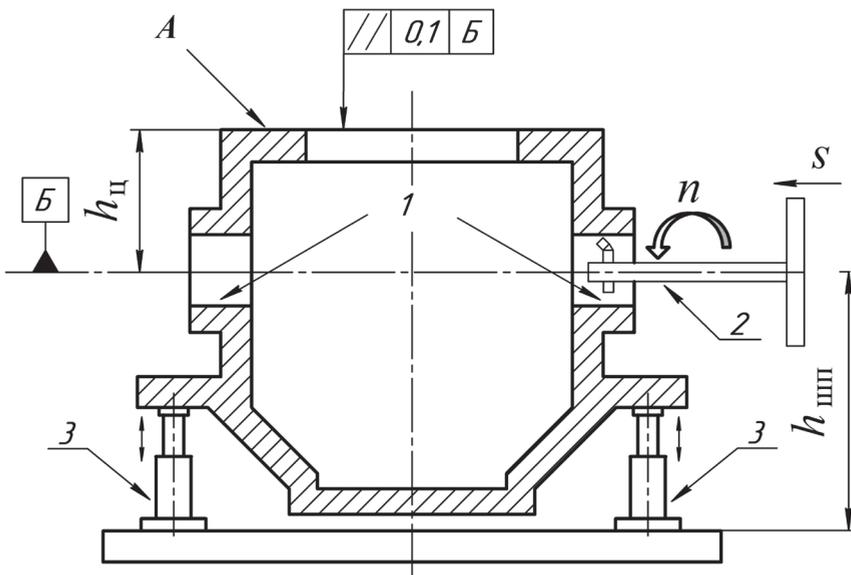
Использование проверочной базы при расточке гнезд подшипников
